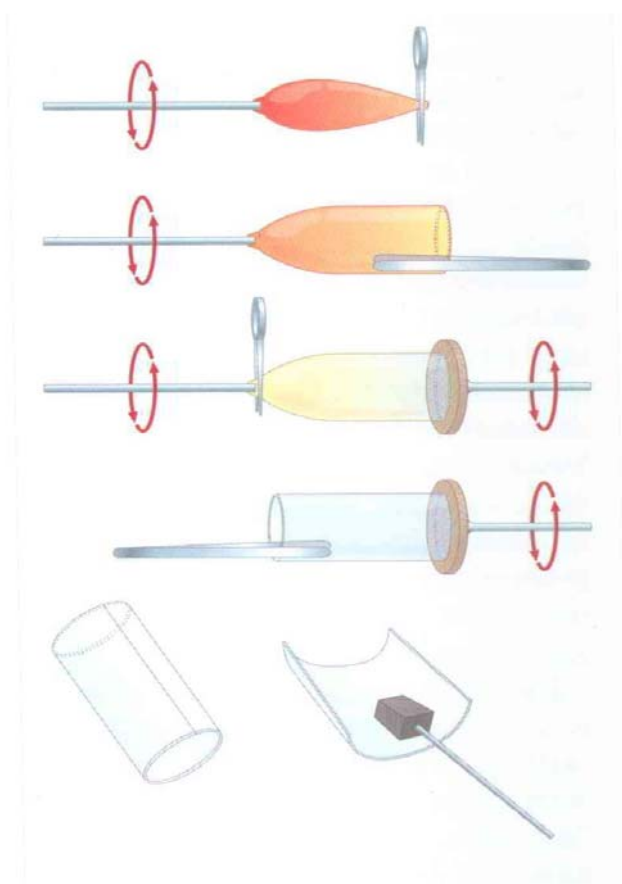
Způsob vyřezání destiček [17]
